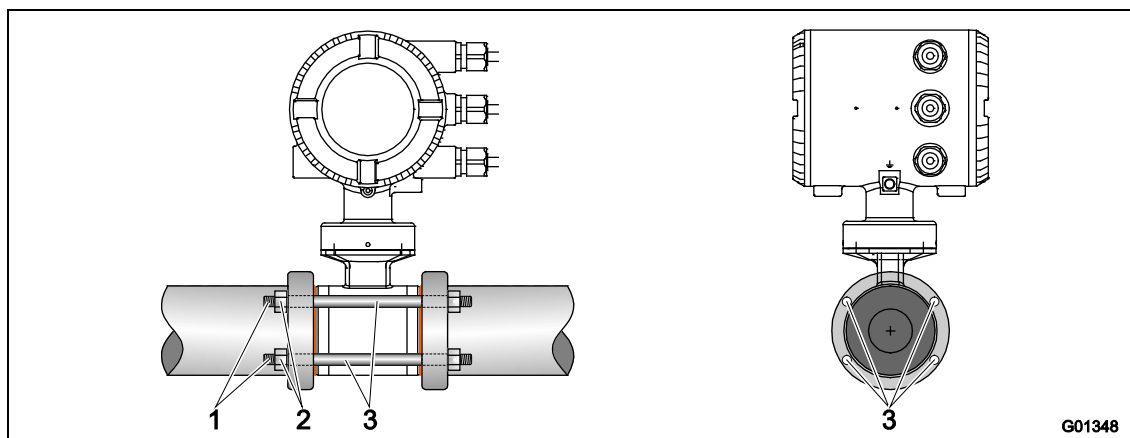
Монтажный комплект для установки конструкции с промежуточным фланцем
